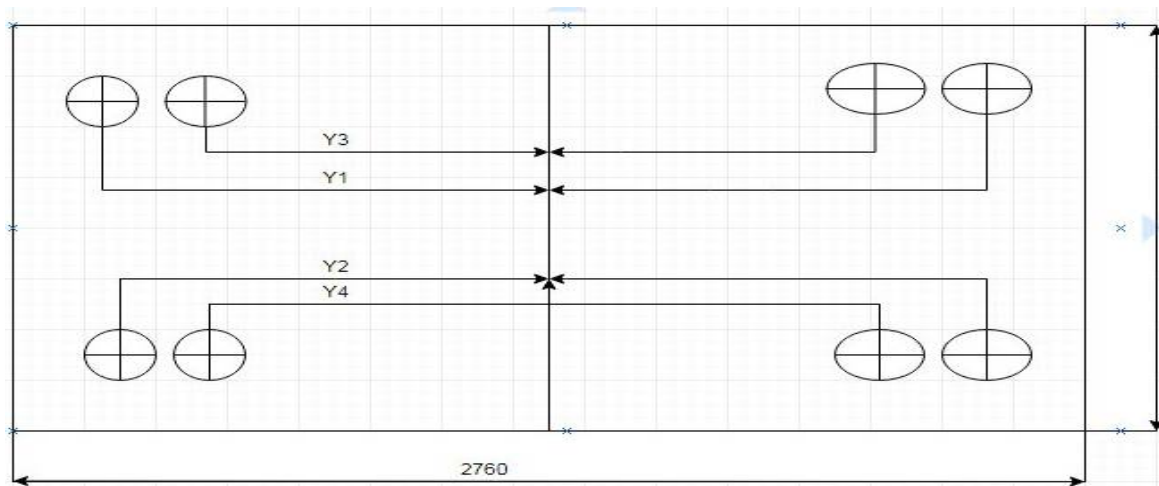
Схема кріплення Кліті 730ПН до фундаменту
